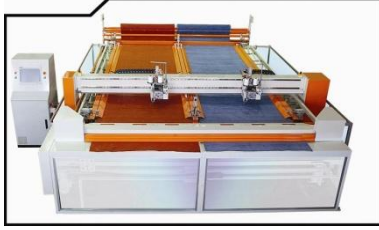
Cutter Seri Kumaş Kesim Makinesi [30].
